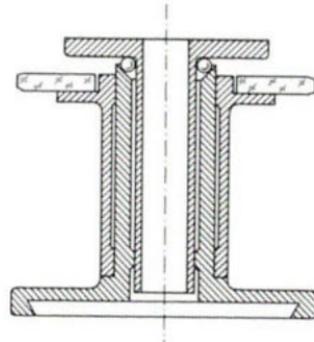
Achssystem mit einem Führungsring und einem Kugellager (Beispiel Wild T2)
